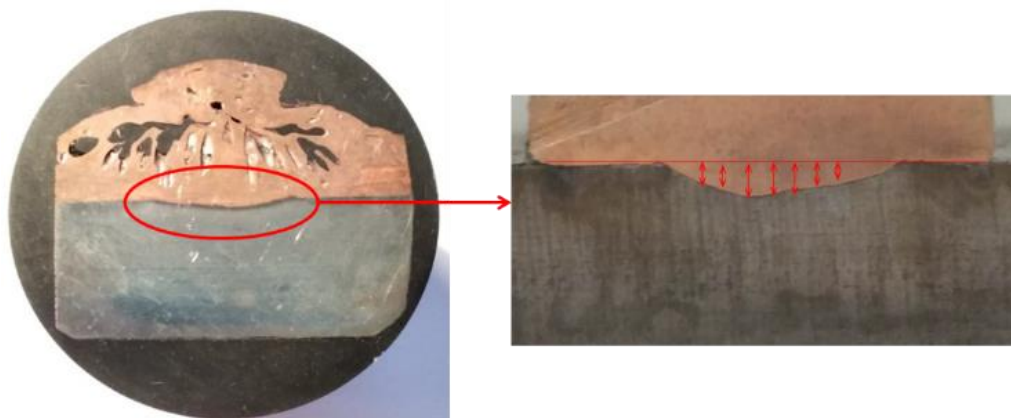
Глубина проплавления основного металла после приварки термитной сваркой вывода ЭХЗ. Образец РЗ, $\times 2$
